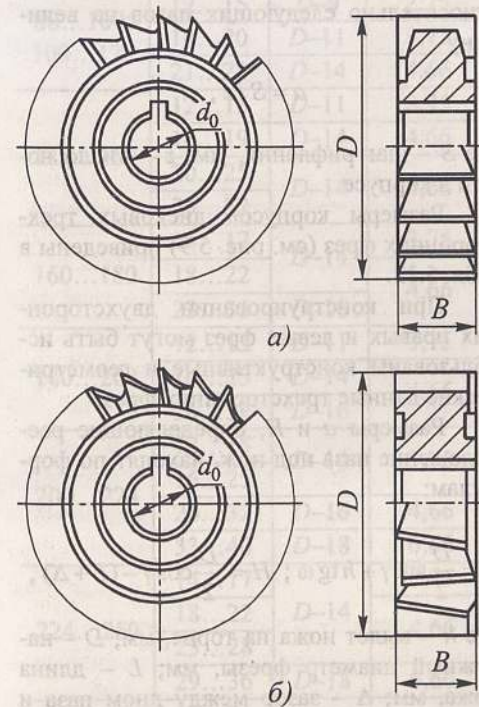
Фрезы дисковые трехсторонние: а – с правыми зубьями, б – с разнонаправленными зубьями
